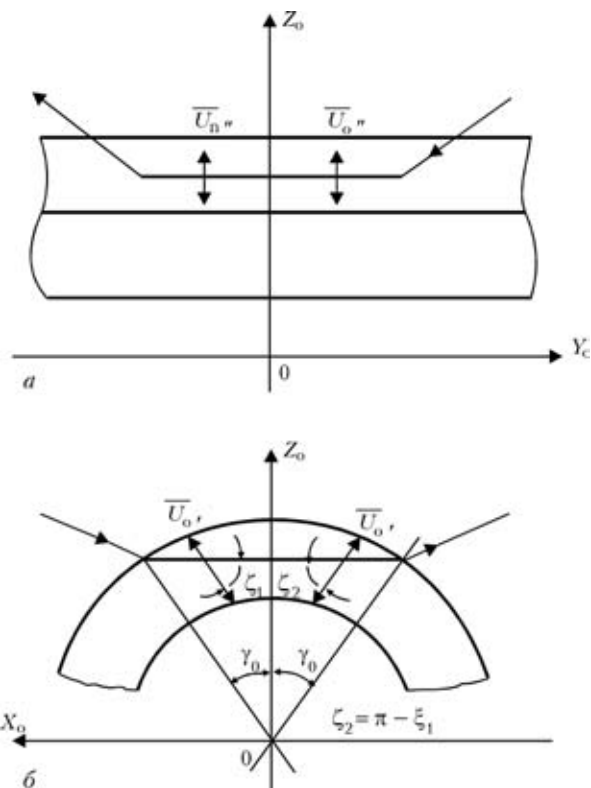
Схема контроля продольных сварных швов или основного металла трубы (прозвучивание поперек образующей) (а) и кольцевых сварных швов (б) хордовыми преобразователями
